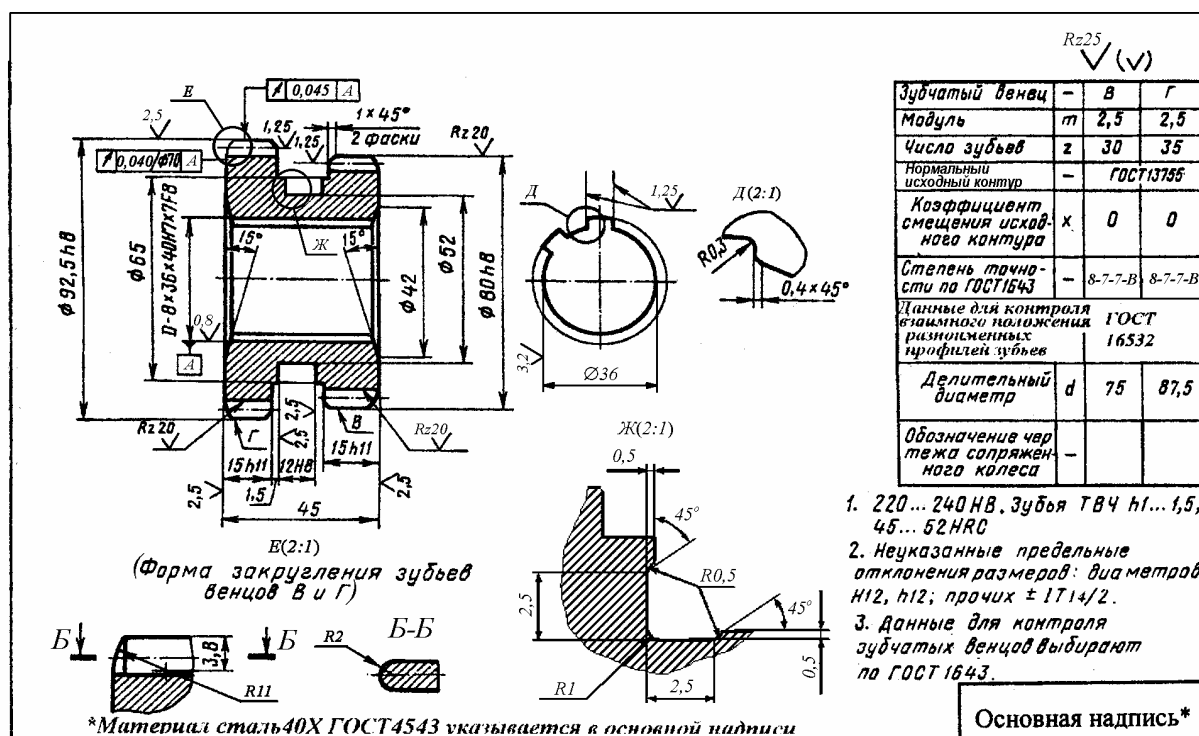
Рабочий чертеж блока цилиндрических прямозубых колес
